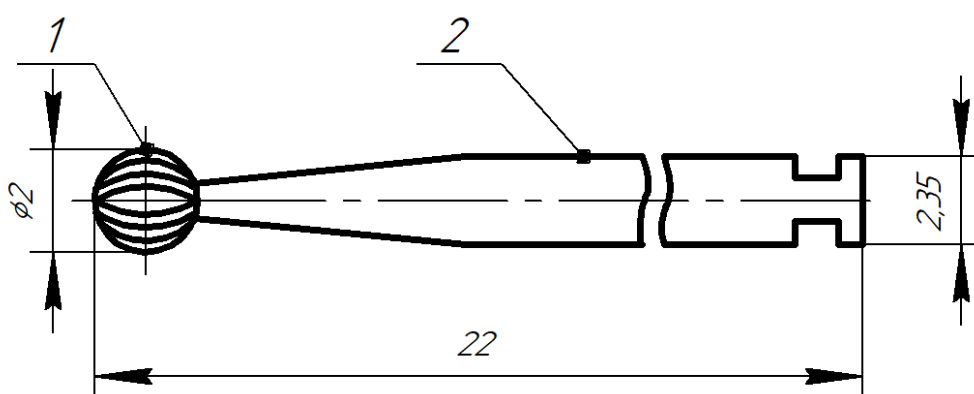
Ескіз кулястої стоматологічної бор фрези: 1. Робоча частина;
